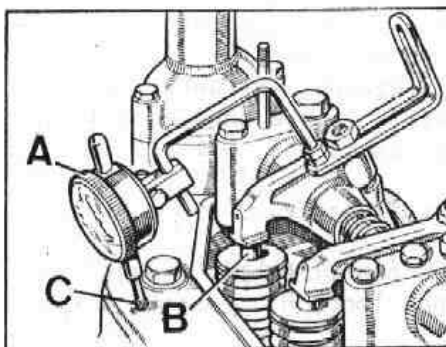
G Comparador de reloj instalado sobre el balancín de la válvula de escape del primer cilindro
